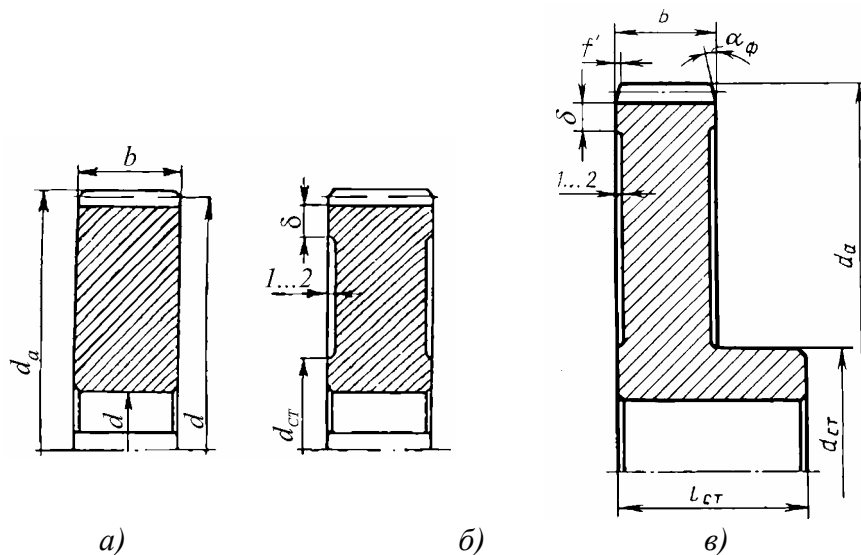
Конструкции цилиндрических зубчатых колес из проката и поковок
